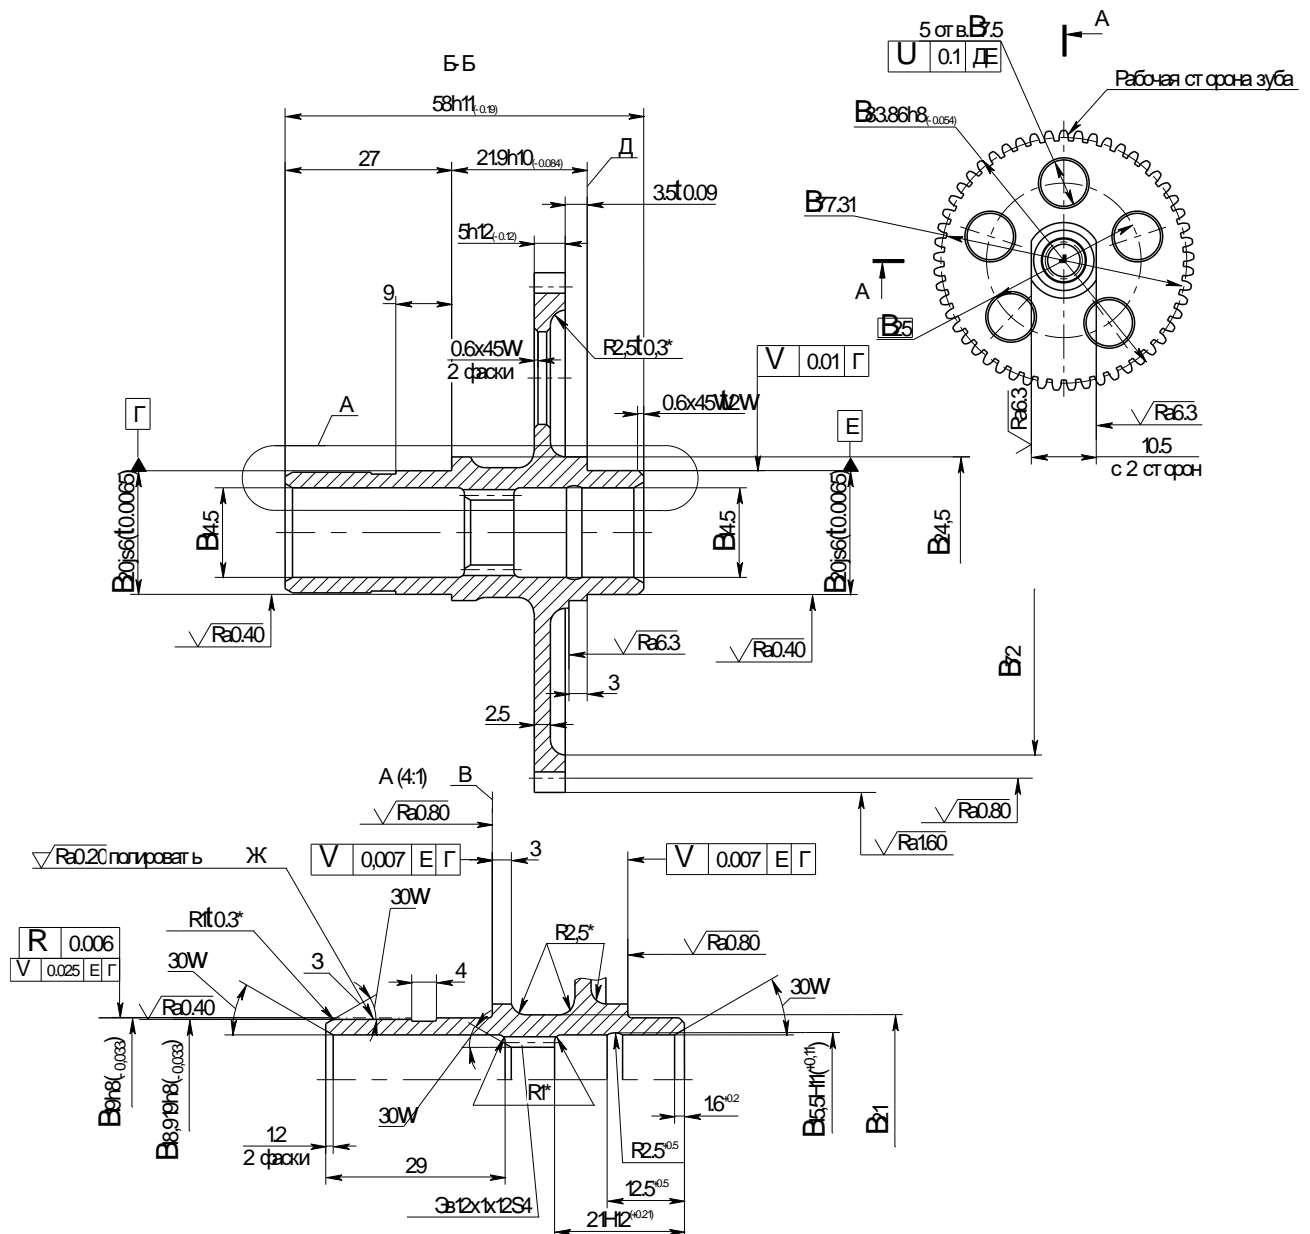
Деталь Шестерня привода насоса-дозатора
